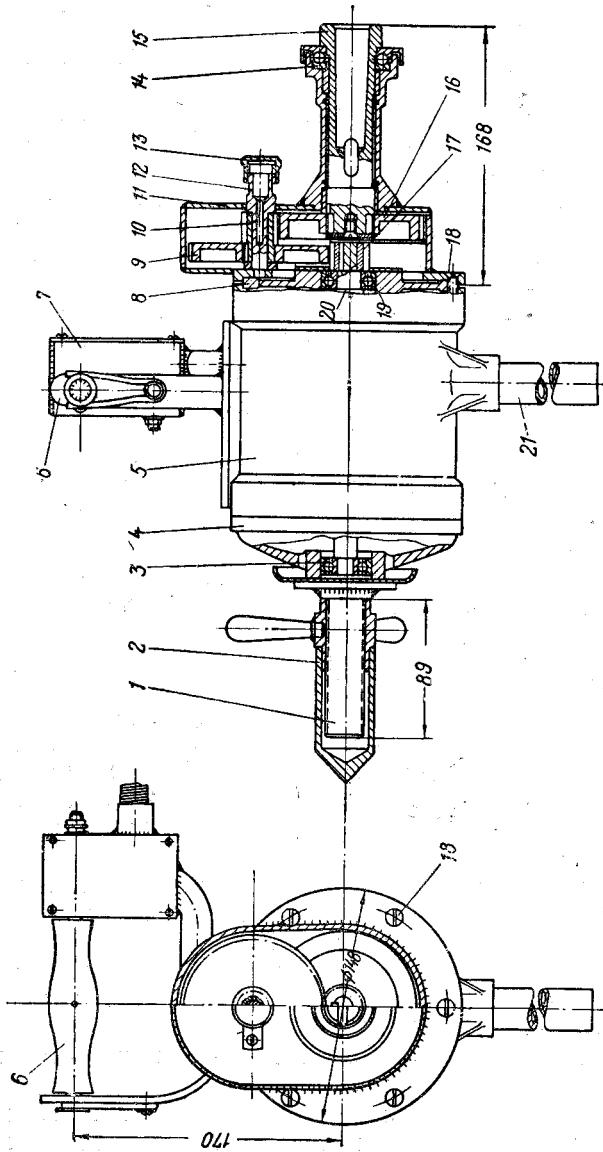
Электродрель И-29, приспособленная для сверления отверстий в рельсах:
